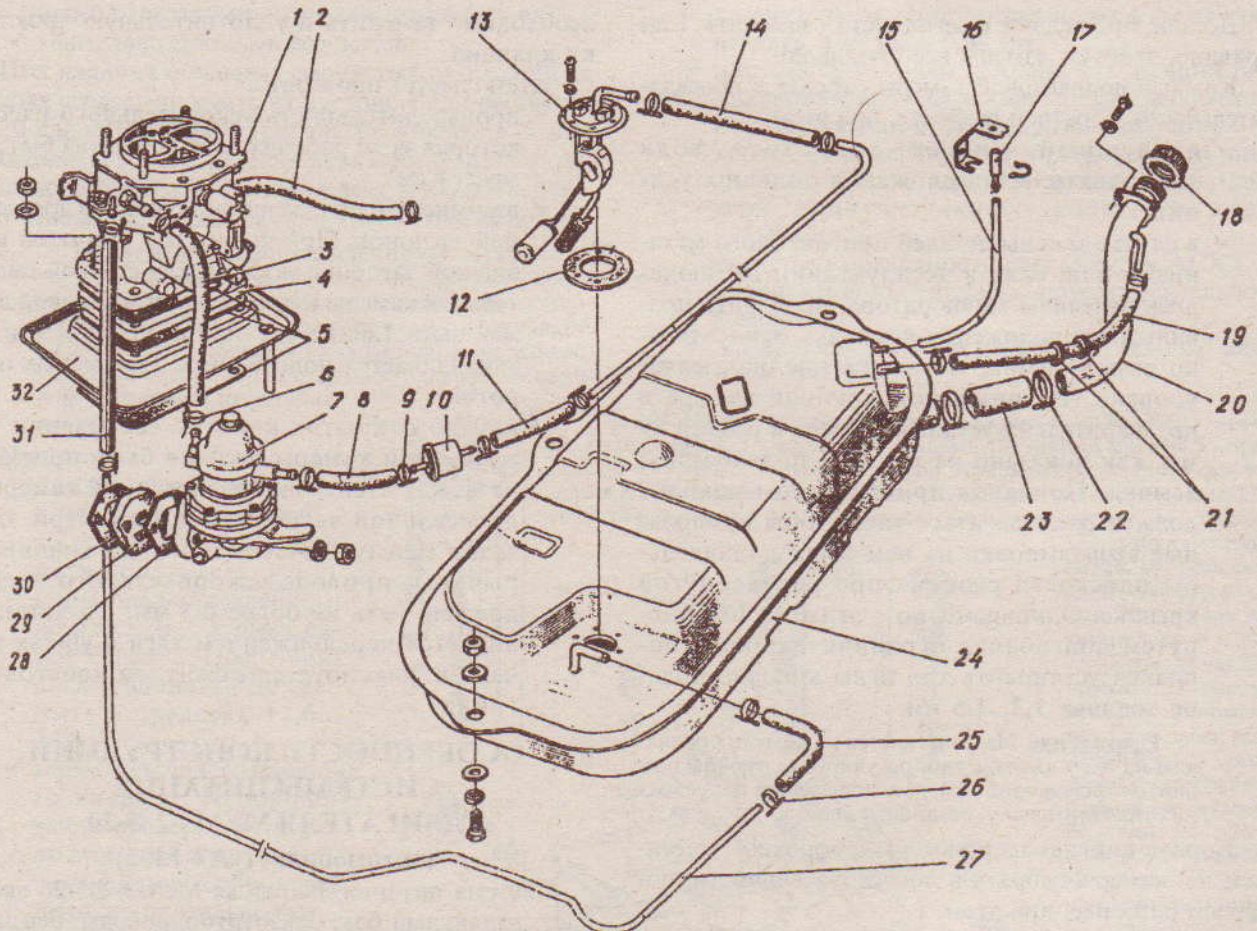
Детали системы питания (карбюратор 21081-1107010): 1 - карбюратор; 2 - шланг к вакуум-корректору; 3 - шланг подачи топлива к карбюратору; 4 - прокладка; 5 - прокладка; 6, 9, 22, 26 - хомуты; 7 - насос топливный; 8, 11 - шланги подачи топлива к топливному насосу; 10 - фильтр тонкой очистки топлива; 12 - прокладка датчика; 13 - датчик уровня бензина; 14 - шланг соединительный; 15 - вентиляционная трубка; 16 - кронштейн; 17 - наконечник вентиляционной трубки; 18 - пробка топливного бака; 19 - шланг воздушный; 20 - трубка наливная; 21 - втулка; 23 - шланг наливной трубки; 24 - топливный бак; 25 - шланг соединительный; 27 - трубка рециркуляции; 28 - прокладка уплотнительная; 29 - прокладка; 30 - прокладка регулировочная; 31 - шланг трубки рециркуляции; 32 - топливосборник
